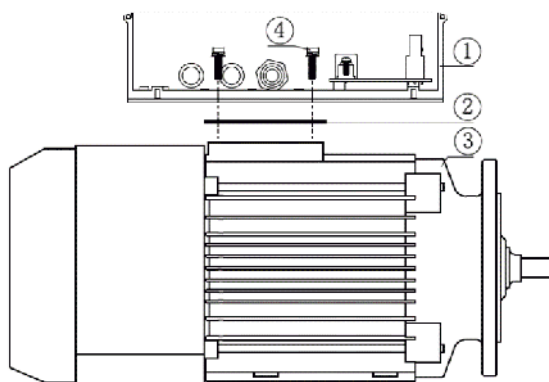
Установка соединительной коробки на двигатель
